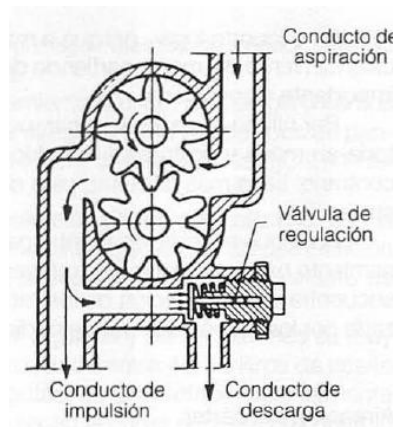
Bomba de engranajes con válvula de regulación de presión.
